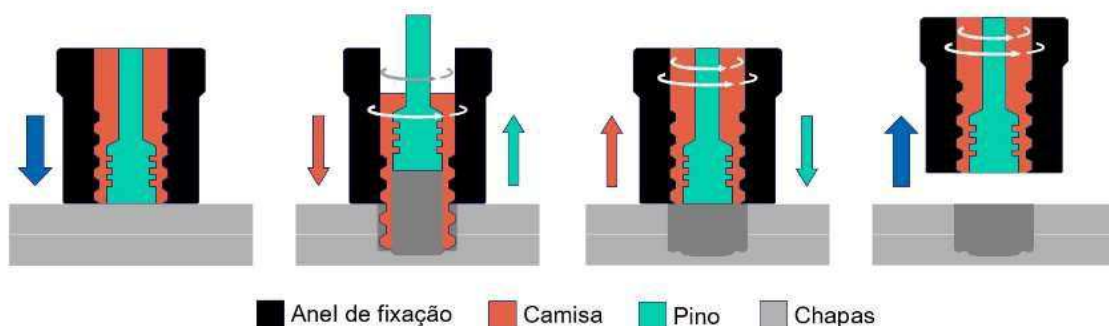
Peças para composição da ferramenta de soldagem FSpW
